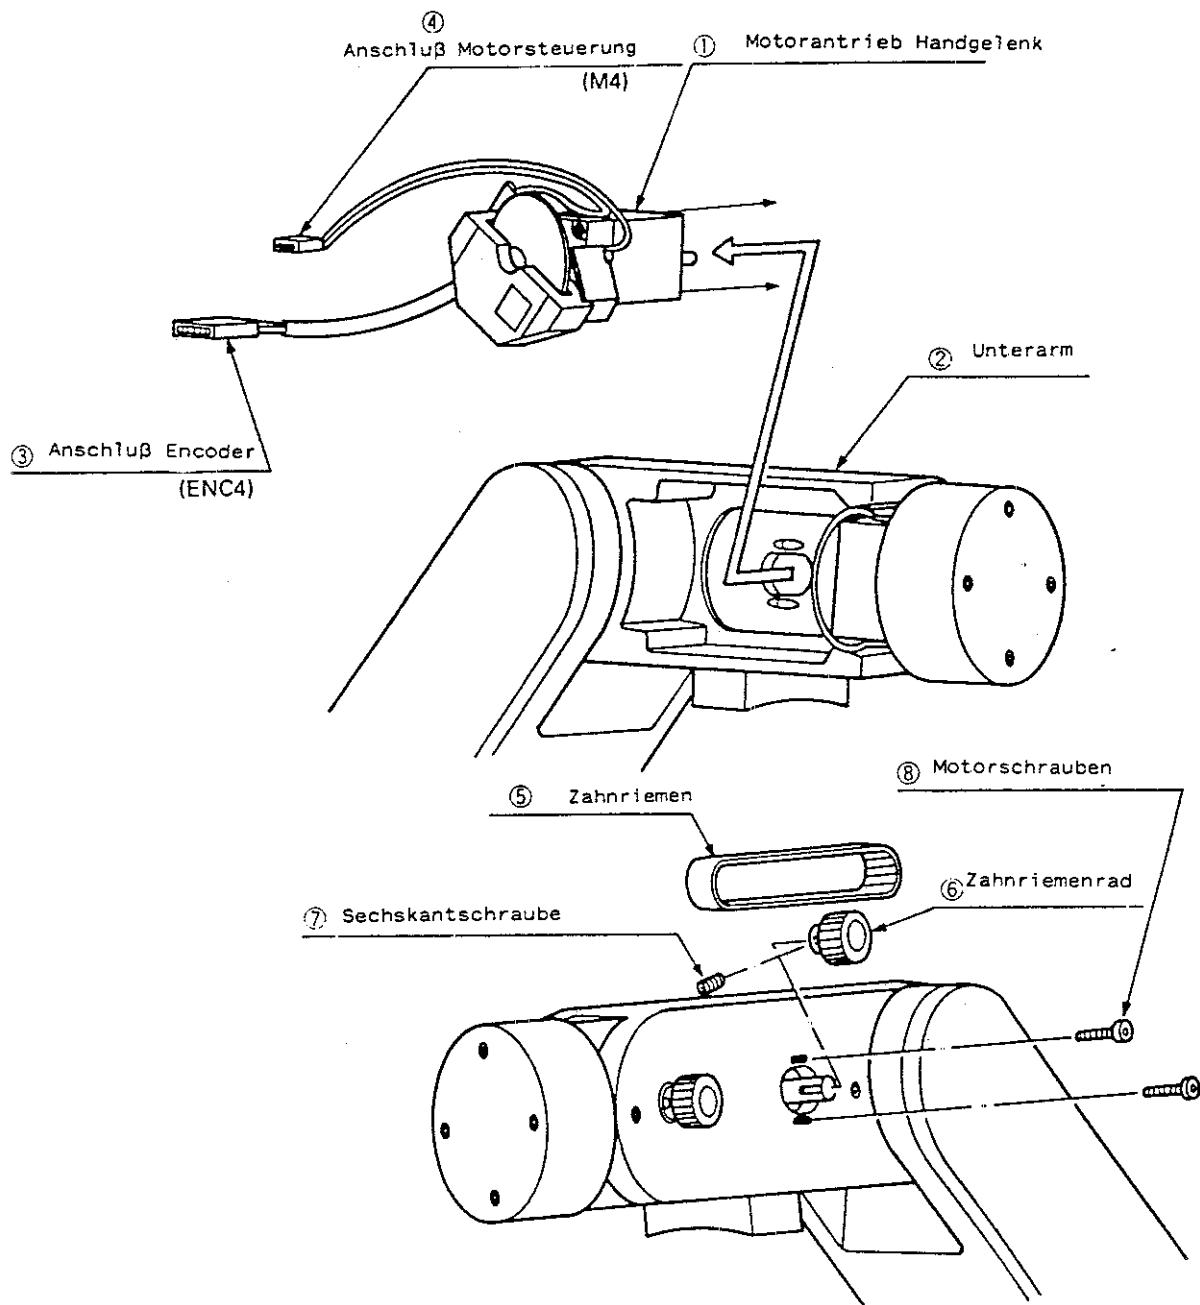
Austausch des Motors vom Handgelenk
